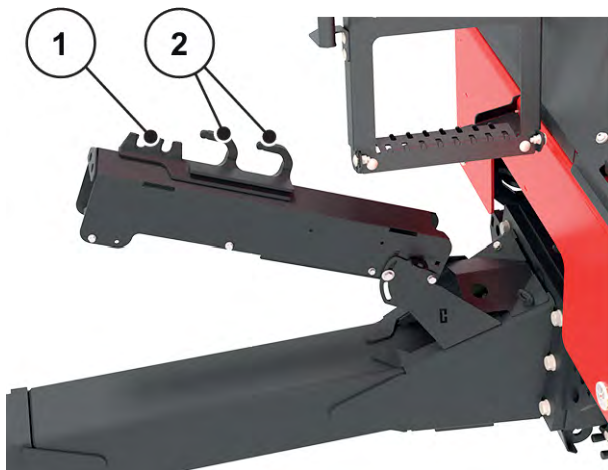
Konsol til opbevaring af kabler, hydraulikslanger og pneumatikledninger
